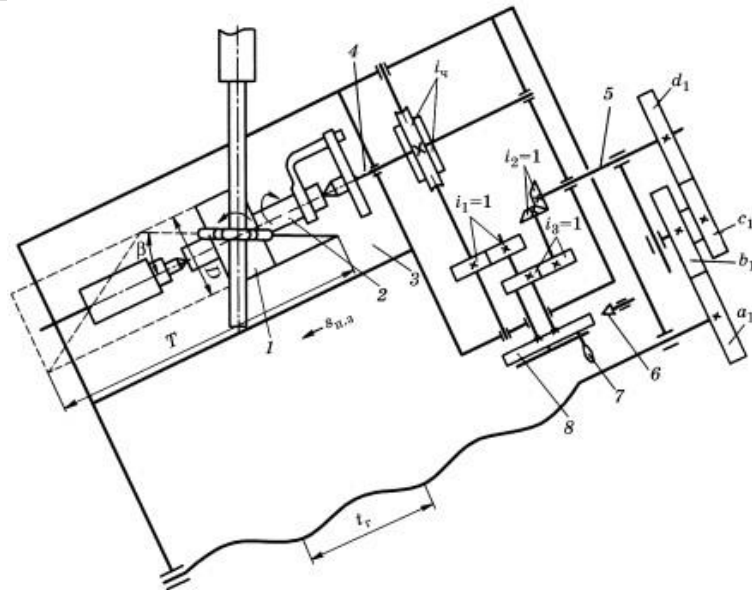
Схема налагодження універсально-фрезерного верстата і ділильної головки на фрезерування гвинтових канавок (косих зубів)
